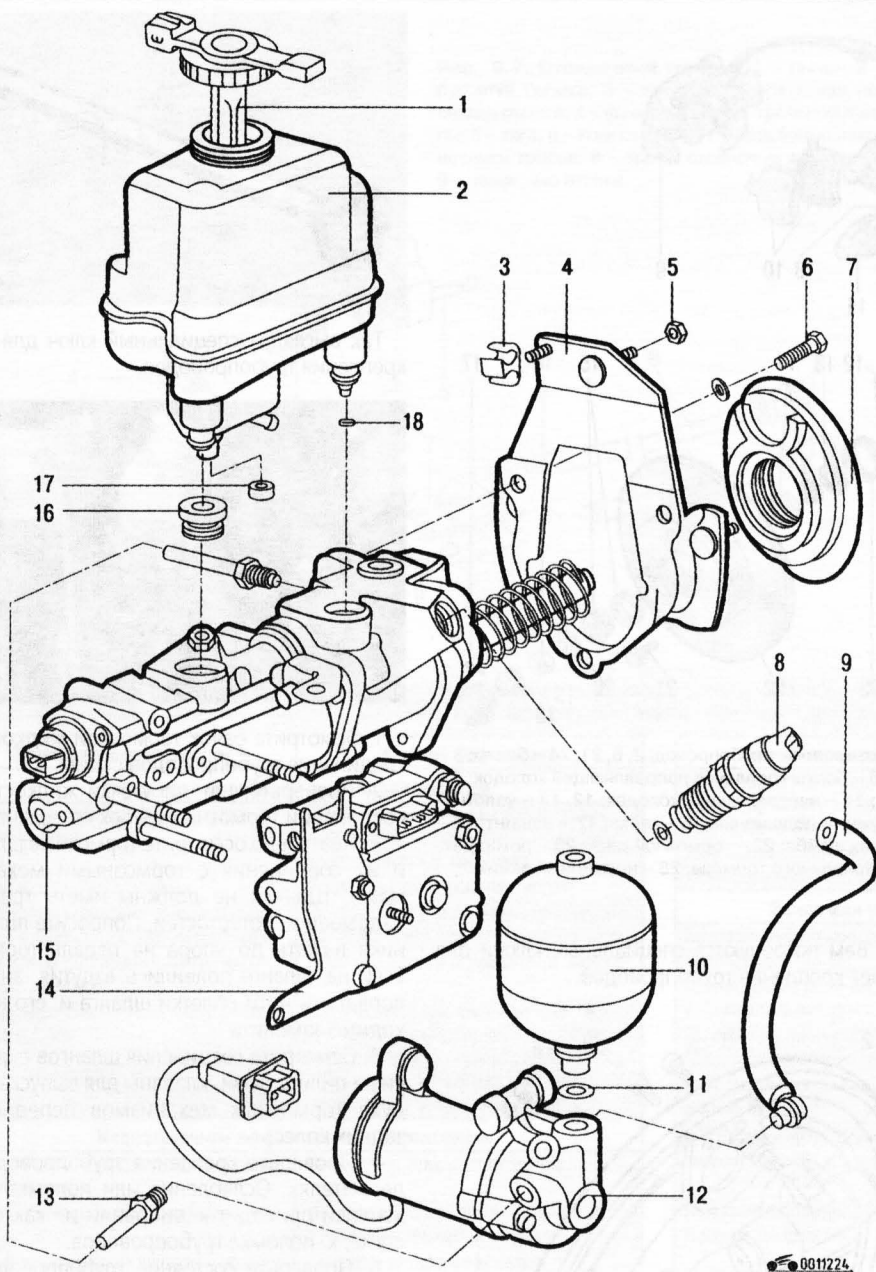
Элементы блока ABS: 1 – пробка; 2 – бачок; 3 – держатель тормозных трубок; 4 – кронштейн; 5 – гайка; 6 – болт; 7 – прокладка; 8 – датчик давления; 9 – соединительный шланг; 10 – гидравлический аккумулятор давления; 11, 18 – уплотнительные кольца; 12 – электрический насос; 13 – тормозная трубка; 14 – блок клапанов; 15 – блок гидравлического усилителя и главный тормозной цилиндр; 16 – соединительная втулка; 17 – втулка
